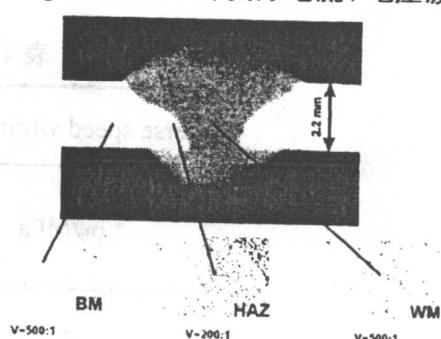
Mg 合金 MIG 焊之焊缝横断面
